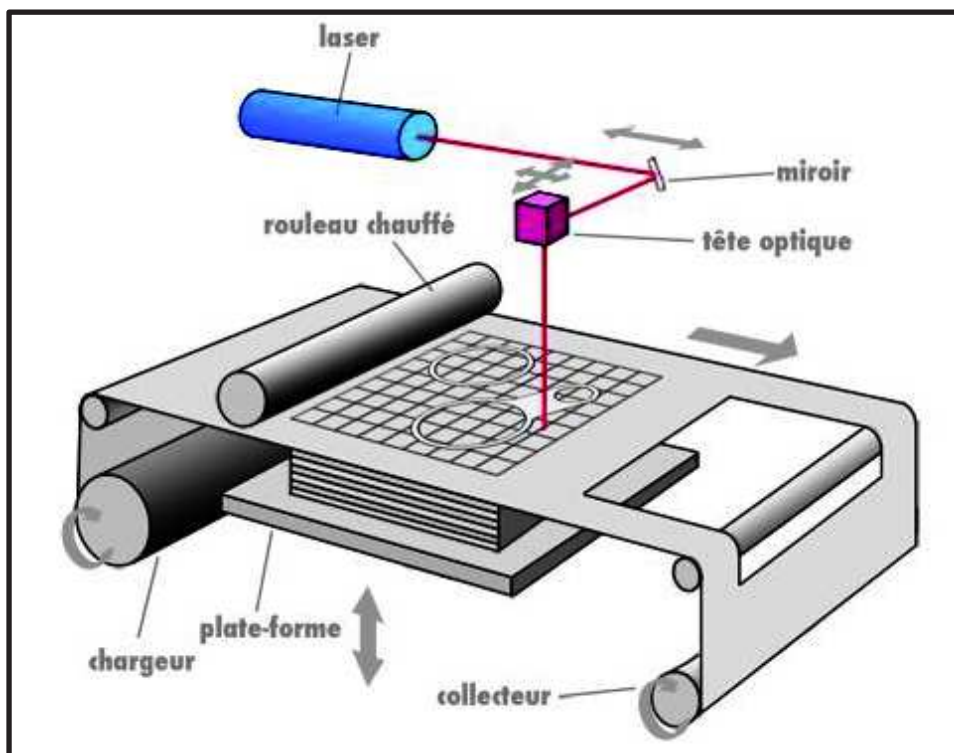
Fabrication additive par laminage de feuilles (LOM). Cette technique consiste à ajouter couche par couche un papier thermocollant découpé par un laser ou une lame. Entre chaque découpage, le plateau descend et une nouvelle feuille adhésive est déroulée. Un rouleau exerce alors une pression afin de la faire adhérer à la surface. Ces étapes sont répétées jusqu'à l'obtention de la pièce 3D. D'après a3dm-magazine.fr.
